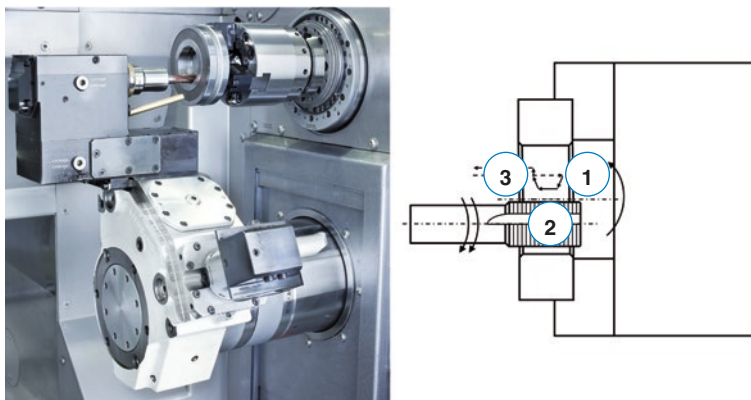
Gewindefräsen im Realbild auf einer Rückseiten-Bearbeitungsstation der SC9-26 (links). [Bildquelle: Schütte] und kinematischer Verfahrensablauf (rechts)
